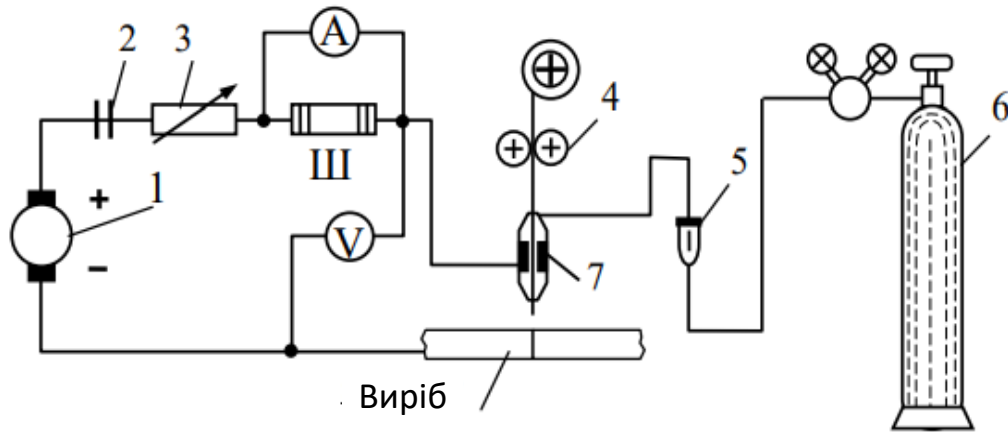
Схема зварювального посту для механізованого дугового зварювання в захисних газах
